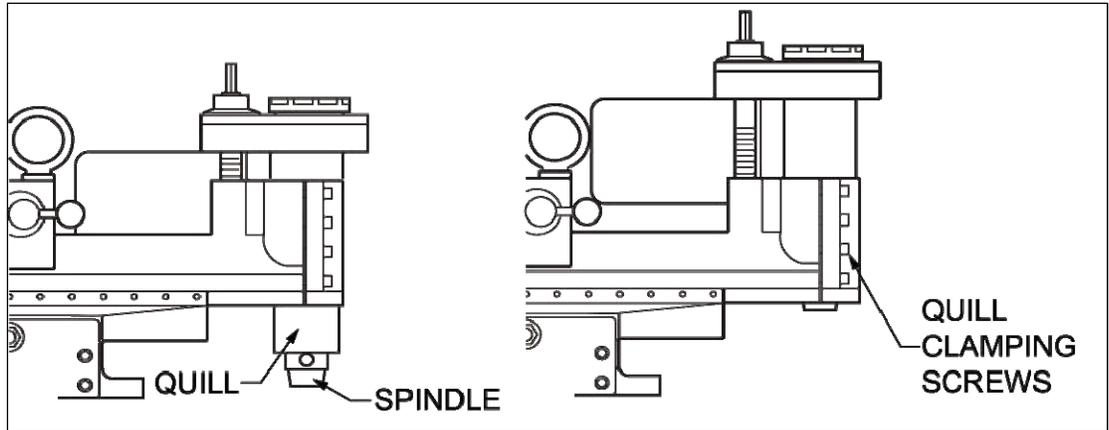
VIS DE SERRAGE DE L'ARBRE CREUX WELDON
